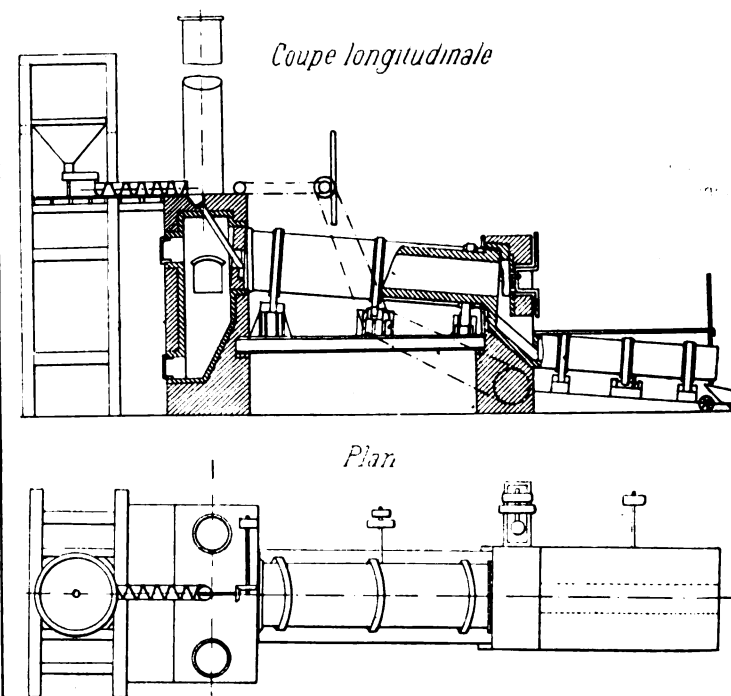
et 2. — Coupe longitudinale et plan du four à ciment.
